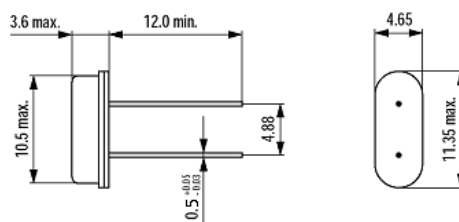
Габаритні розміри кварцового резонатора типу РК-169
